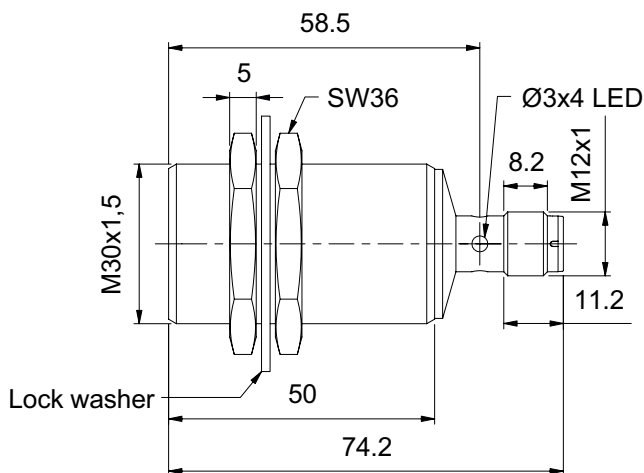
Lange Ausführung, bündiger Einbau, Steckversion
